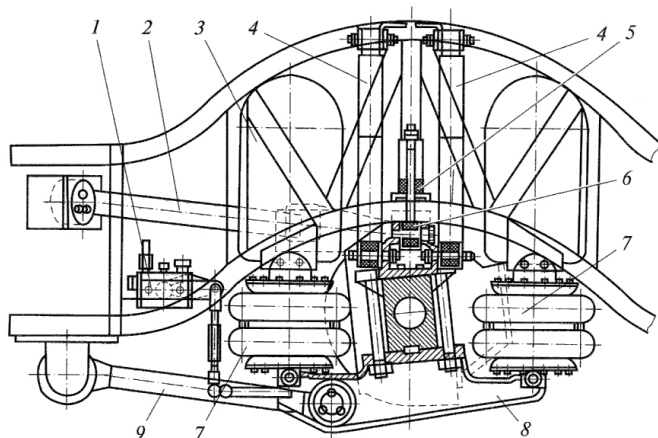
Пневматическая подвеска автобуса: 1 — регулятор положения кузова; 2, 9 — продольные штанги; 3 — резервуар воздуха; 4 — амортизаторы; 5, 6 — буферы; 7 — баллоны; 8 — кронштейн
